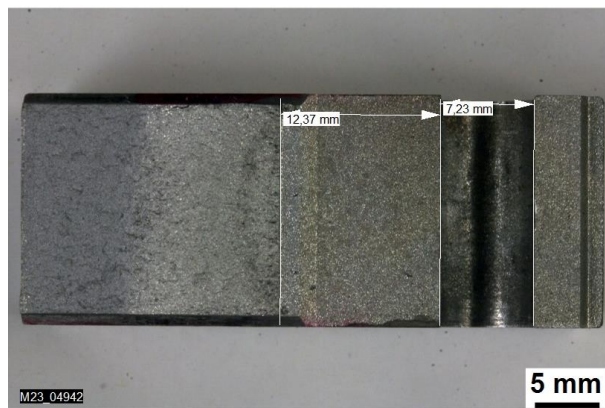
Probe 5.b Makroaufnahme Probenhälfte mit ausgemessener Länge von Lastangriffslinie bis zur erodierten Kerbe
